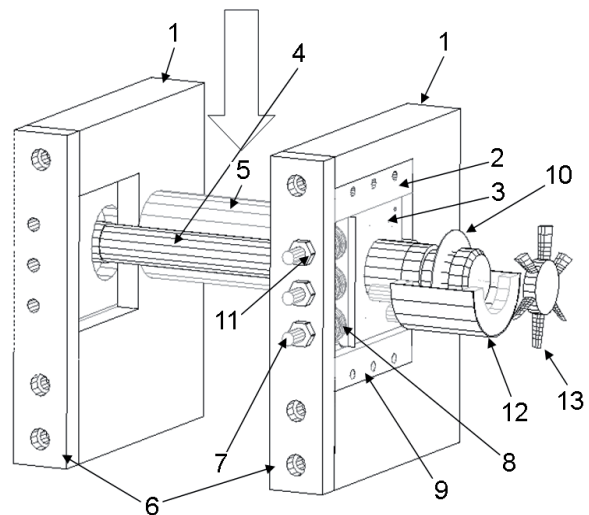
Parte activa del Molino Ultrasónico de Rodillos de Alta Presión (MURAP). En el diagrama: 1 Muros soportantes (acero estructural), 2 Rodamientos lineales, 3 Soporte rodamientos, 4 Rodillo ultrasónico, 5 Rodillo pasivo, 6 Pernos Parker de montaje, 7 Control de tensión, 8 Resortes tensores, 9 Soportes rodamientos, 10 Electrodo rotatorio, 11 Tuercas fijación holgura, 12 Cáster, 13 Ventilador.
